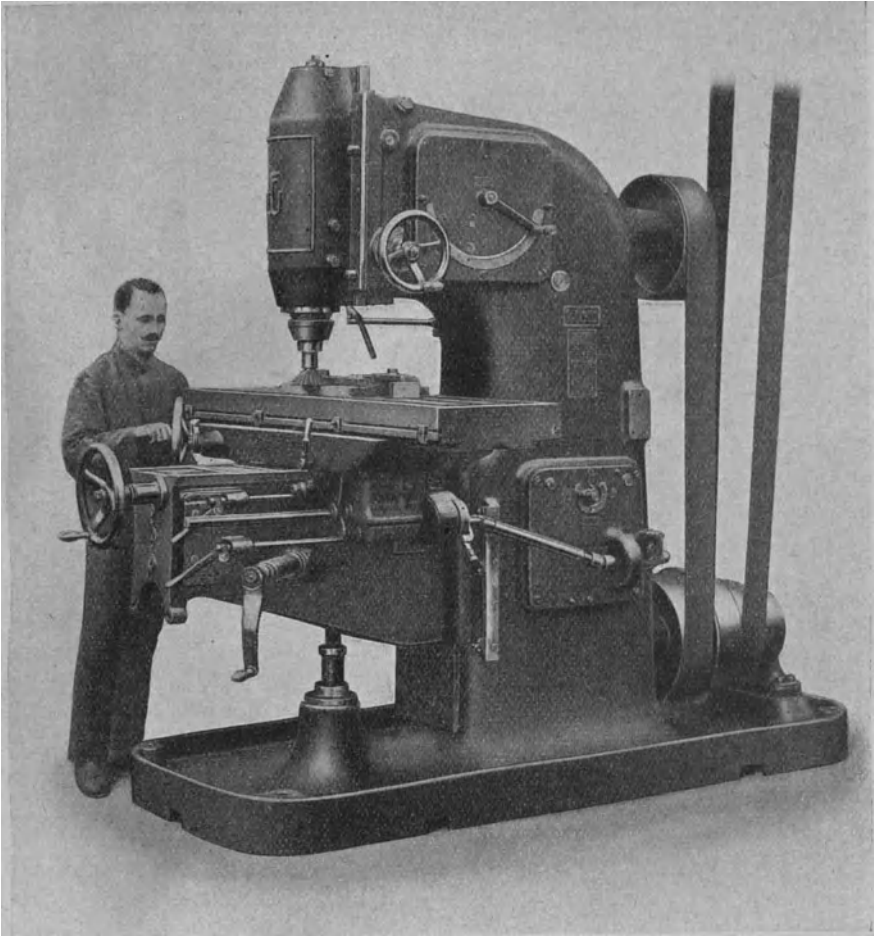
Sentracht-Fräsmaschine von Fritz Werner.
